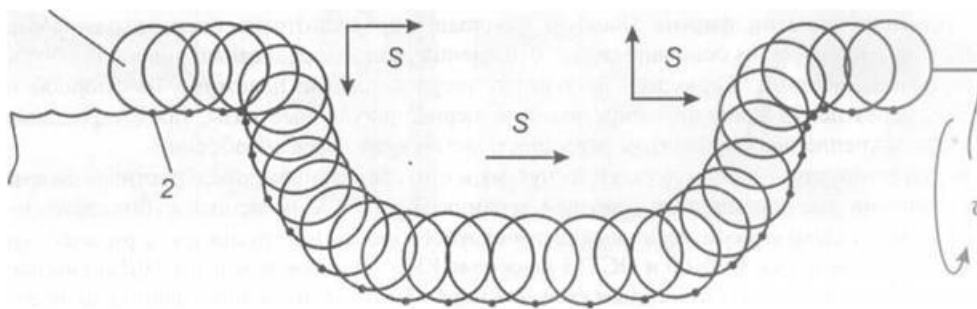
Схема оброблення рівчака прокатного валка різцем із круглою різальною пластиною: 1 – різальна пластина, 2 – робоча вершина різця
